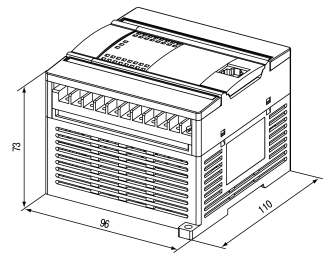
Габаритный чертеж ПР110-х.12х.8х
